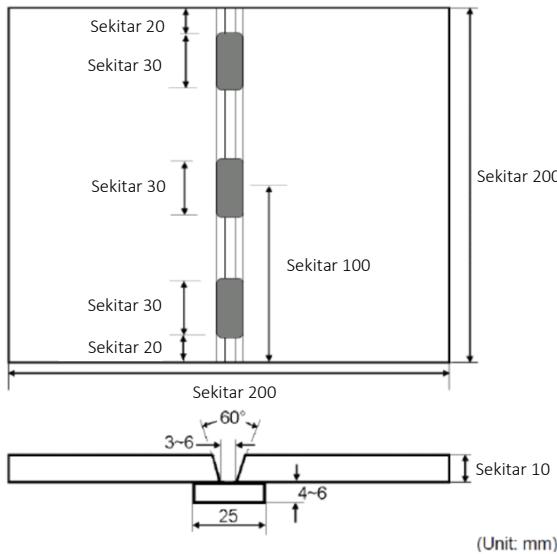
Dimensi benda uji untuk las fillet di pelat
